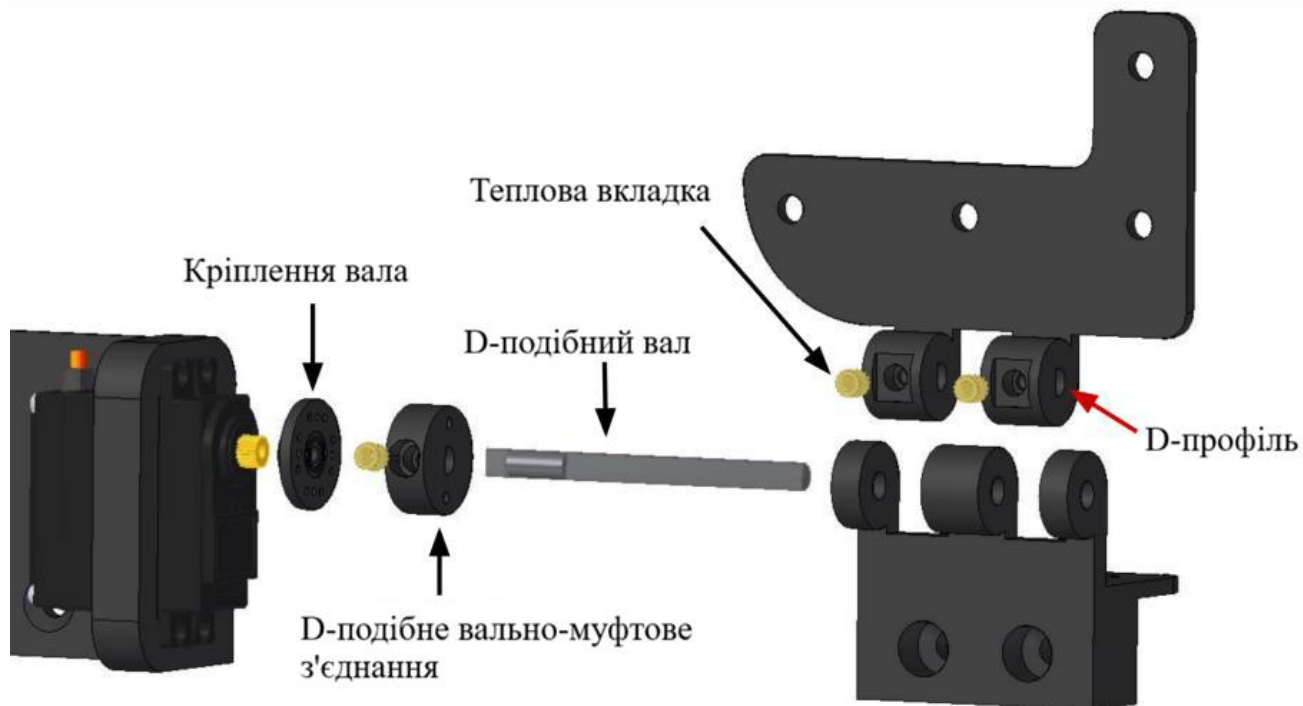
Принцип роботи механізму руху коротких дошок
